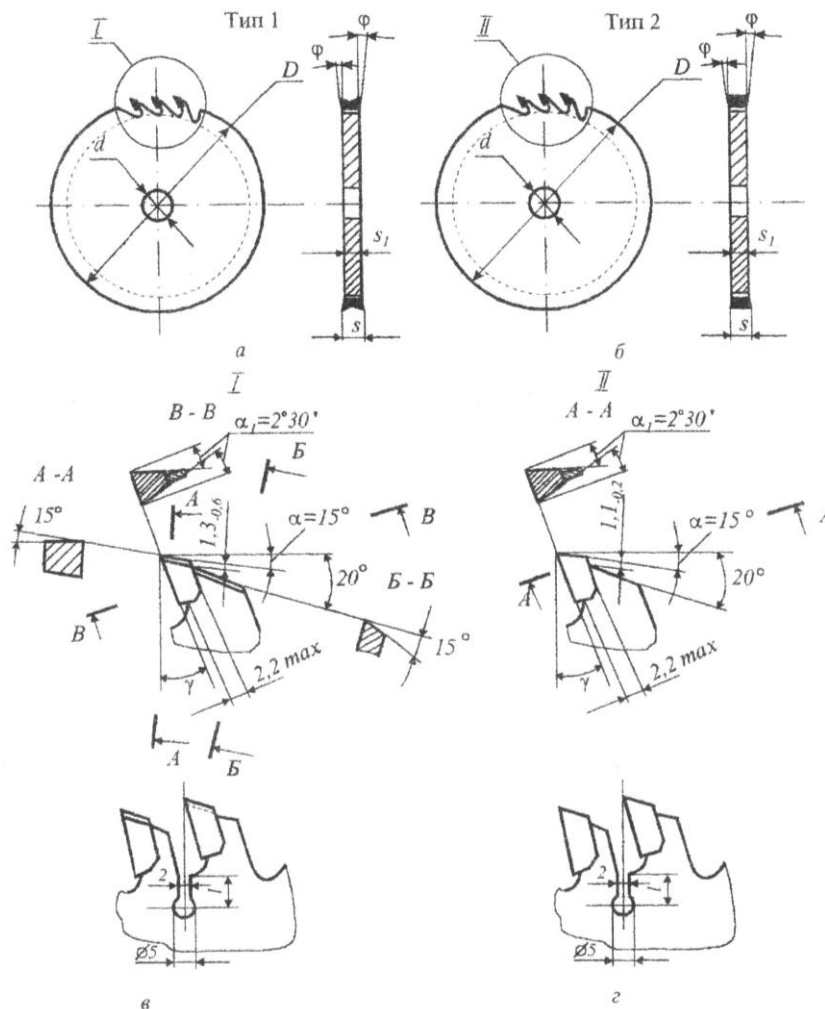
Кругла пилака з твердосплавними пластинами: а – тип 1; б – тип 2; в – зуби пилки типу 1; г – зуби пилки типу 2
